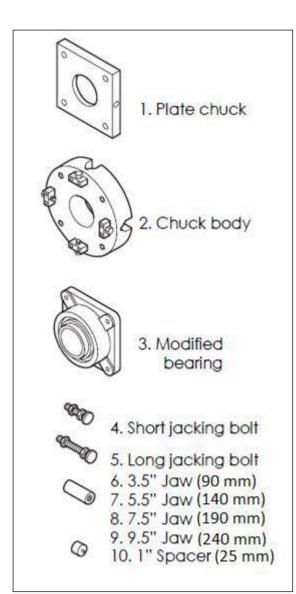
MONTAJE DI DE COMPONENTE DE RODAMIENTO
